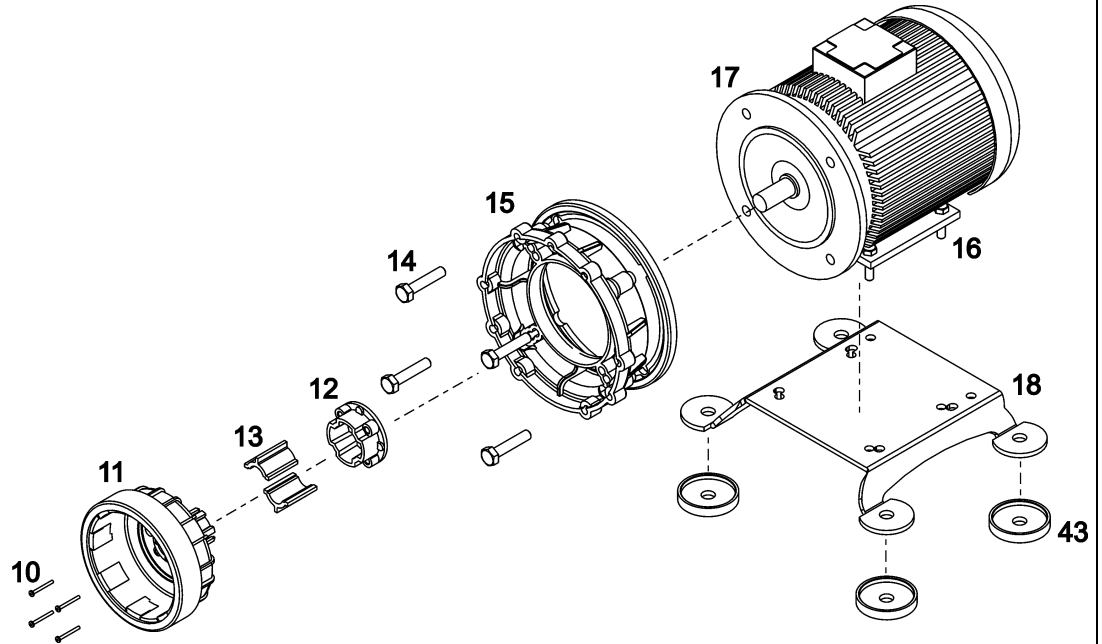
A – DEMONTAGE DE LA POMPE : ENSEMBLE MOTORISATION
